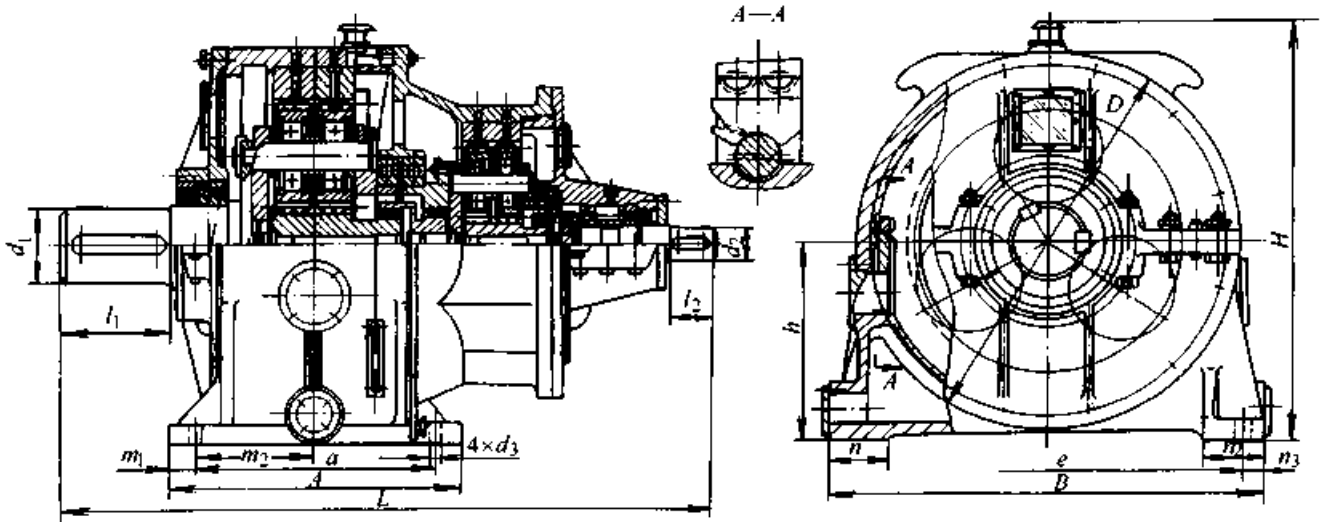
NGW 型非标准行星齿轮减速器结构
